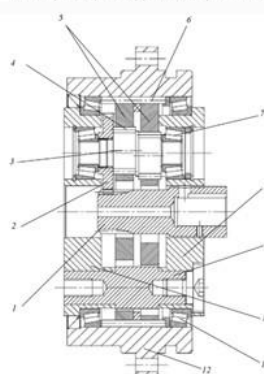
Конструкція планетарно-цивкового редуктора типу 2К-В
